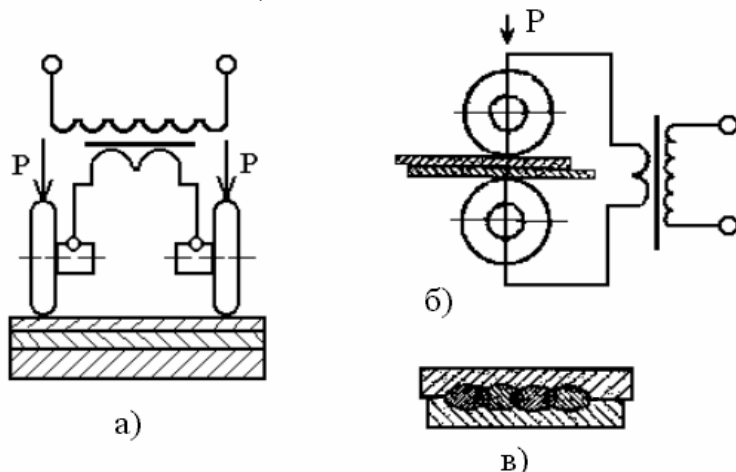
Схема роликовой контактной сварки:
